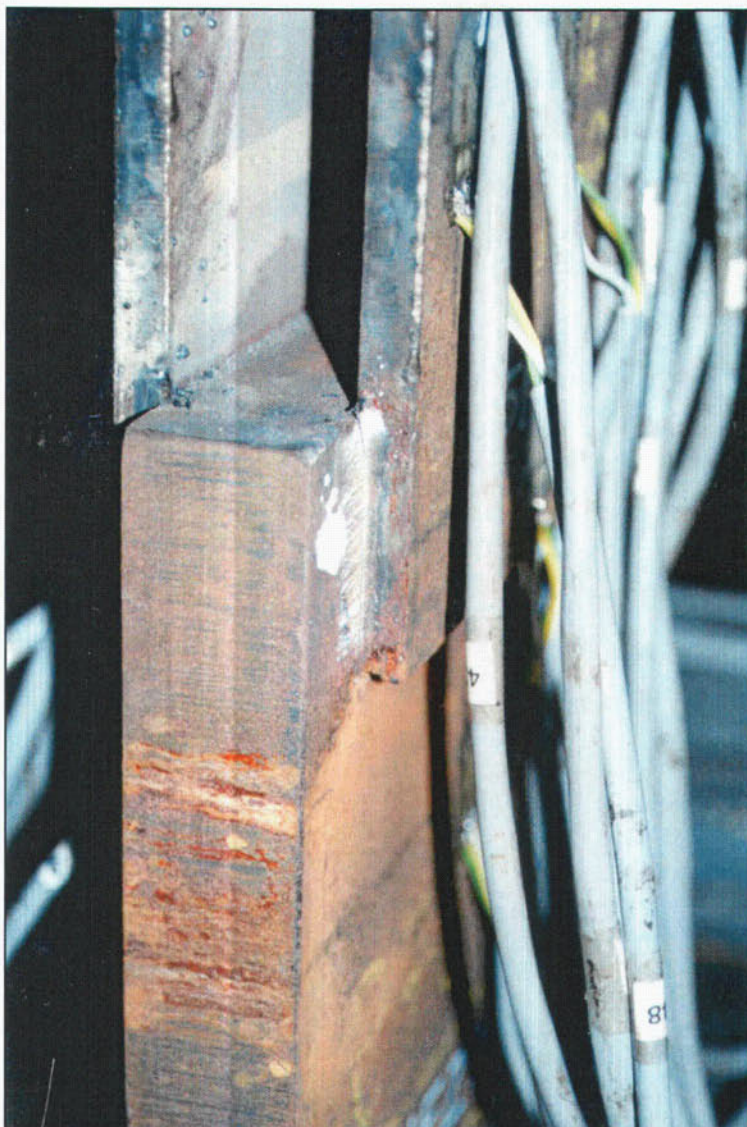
Detalle de rotura de soldadura en la probeta 1T tras el ensayo de tracción, por el plano de garganta.
